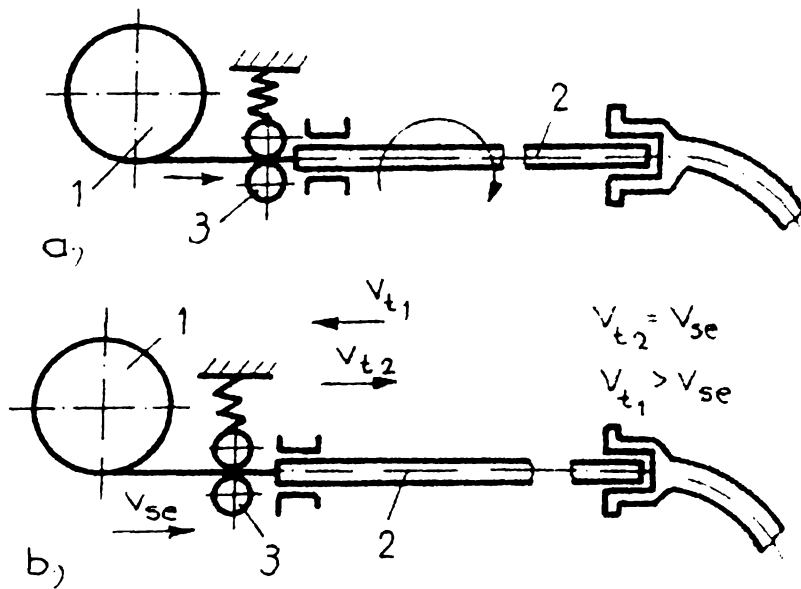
Mecanism cu rotirea sau vibrarea axială a tubului flexibil
